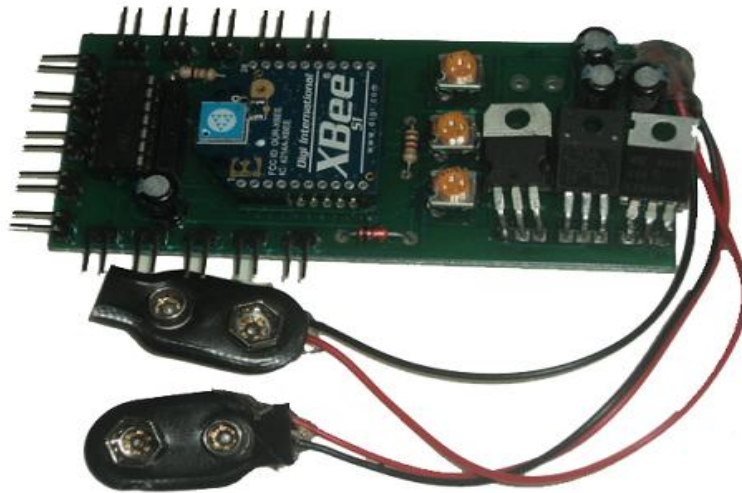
Circuito impreso de la parte frontal del Módulo Remoto
